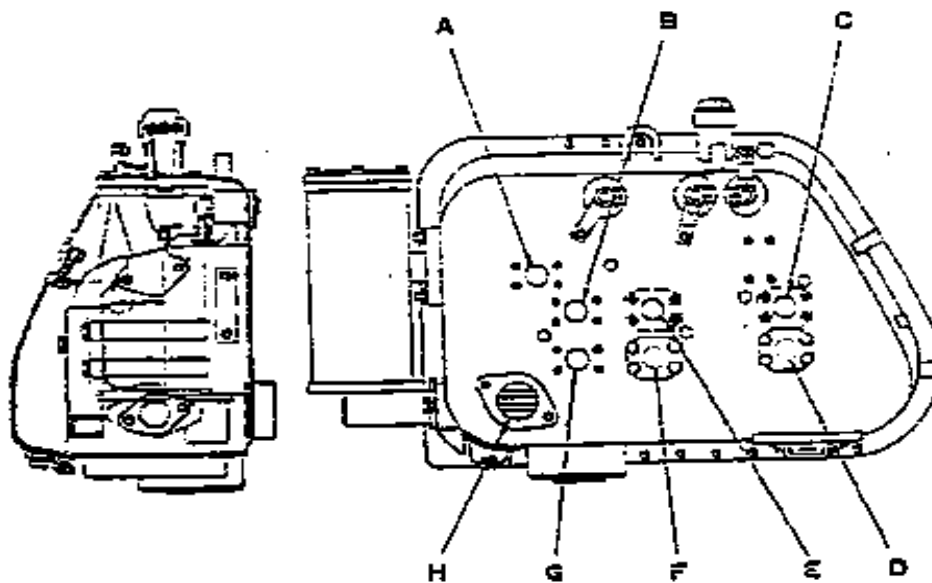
Konstruksi *Hydraulic Tank* (3 dimensi)
